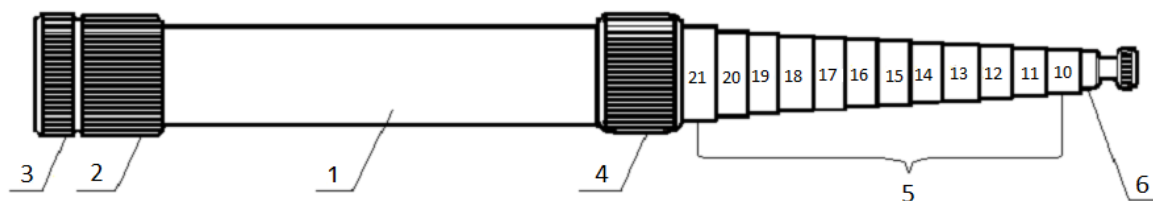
Устройство «инструмент для формирования спиральных венозных графтов»: 1 – корпус; 2 – проксимальный конец корпуса; 3 – заглушка с рифлёной поверхностью; 4 – дистальный конец корпуса; 5 – система тонкостенных трубок диаметром 10–21 мм соответственно; 6 – хвостовик с рифлёной поверхностью
